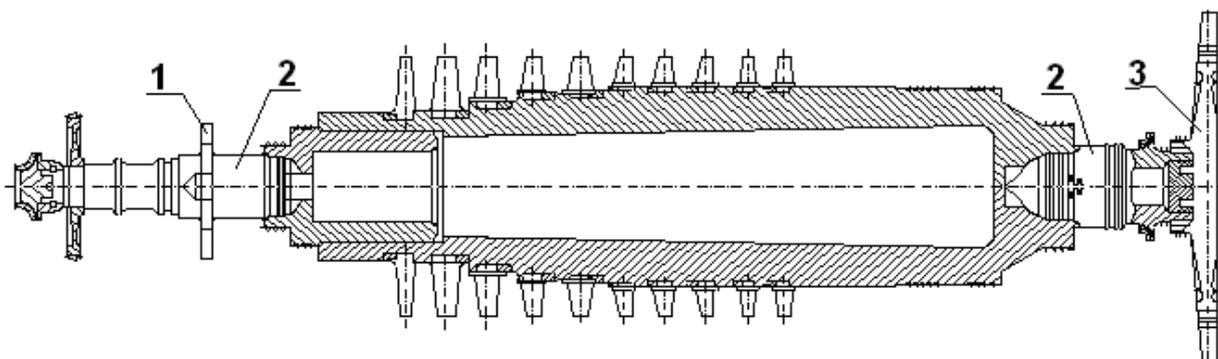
Ротор ТВД. 1 – диск упорный, 2 – опорные шейки подшипников, 3- диск ТВД.
